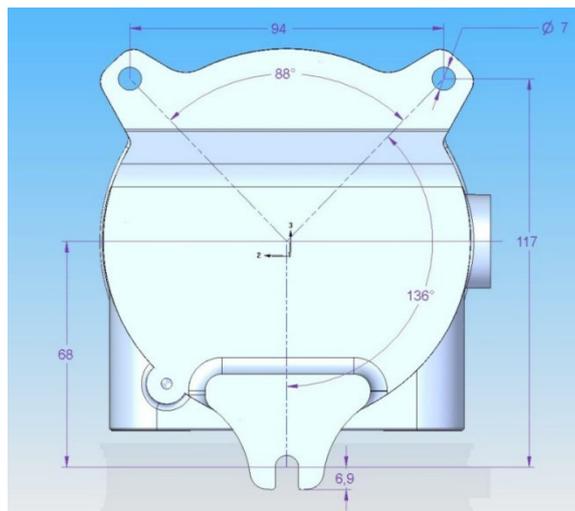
Dimensions de perçage pour fixation du support (mm)
